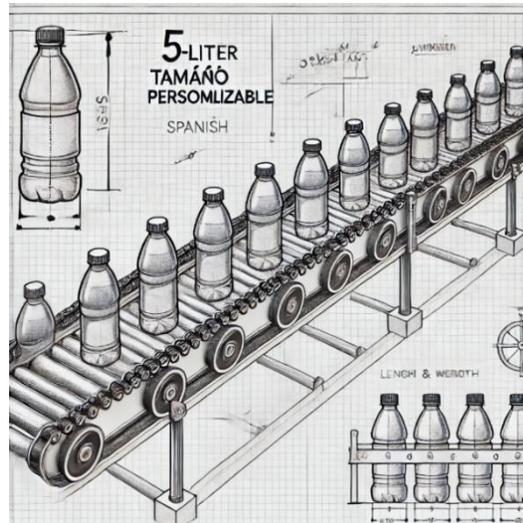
Diseño y dimensionamiento de Llenadora de botellas
